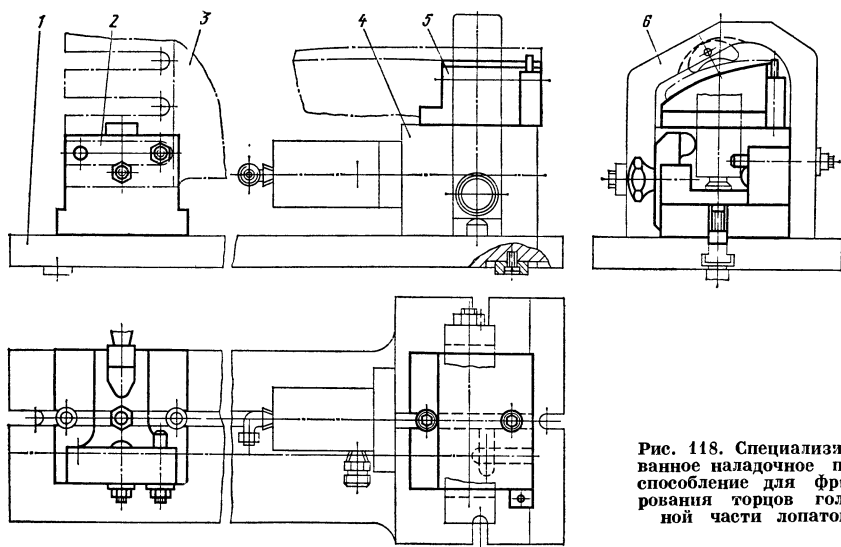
Специализированное наладочное приспособление для фрезерования торцов головной части лопаток
